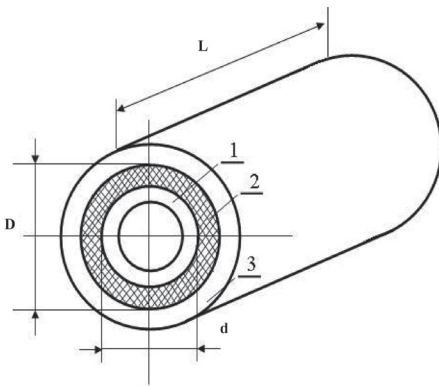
Схема шарніру гумово-металевого: 1 – внутрішня металева втулка; 2 – гумовий шар; 3 – зовнішня металева арматура; L – довжина гумового шару; d – внутрішній діаметр гумового шару; D – зовнішній діаметр гумового шару
